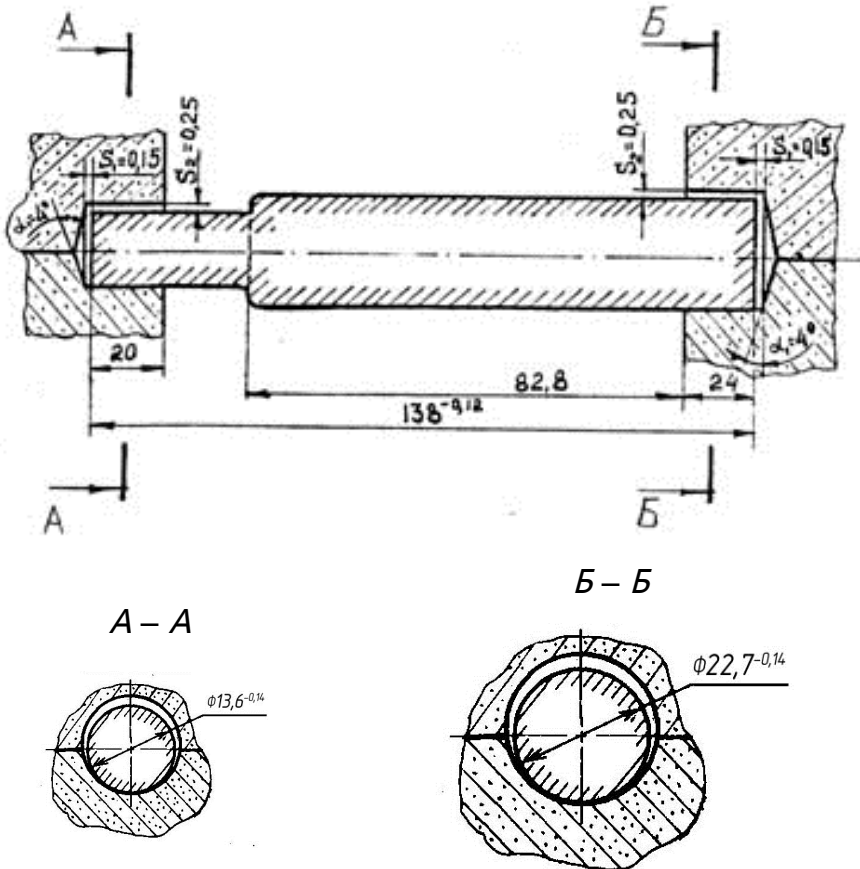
Стрижень і знаки ливарної форми виливка “Супорт”
